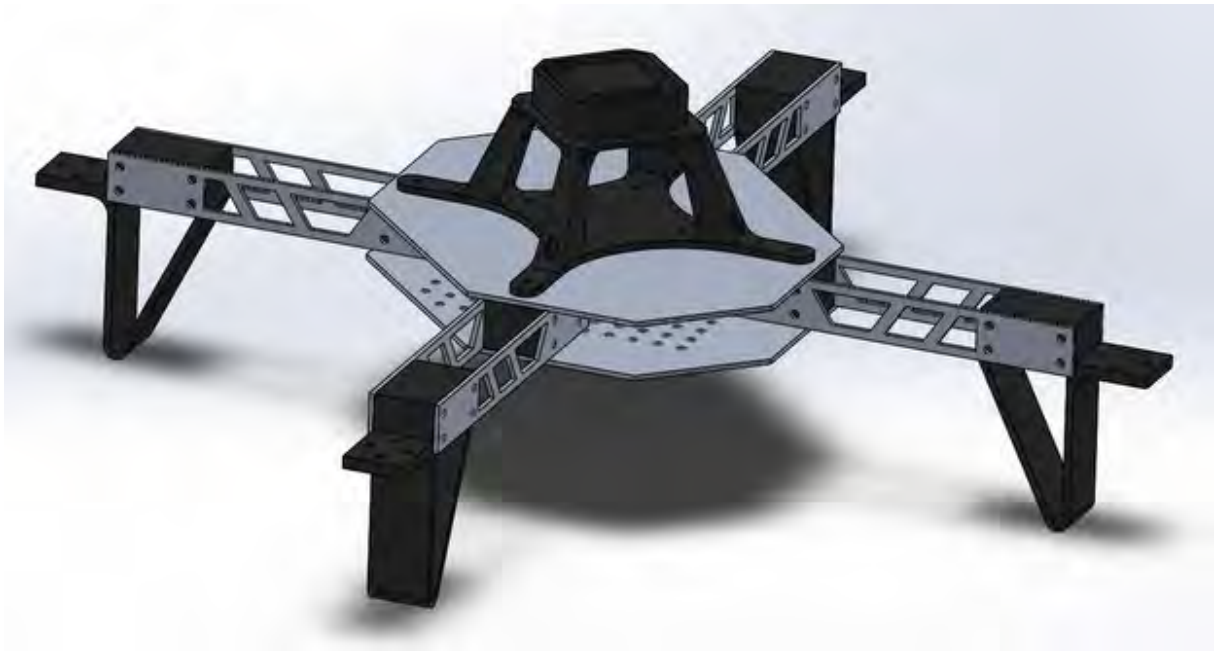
Estructura compuesta de aluminio y piezas impresas
